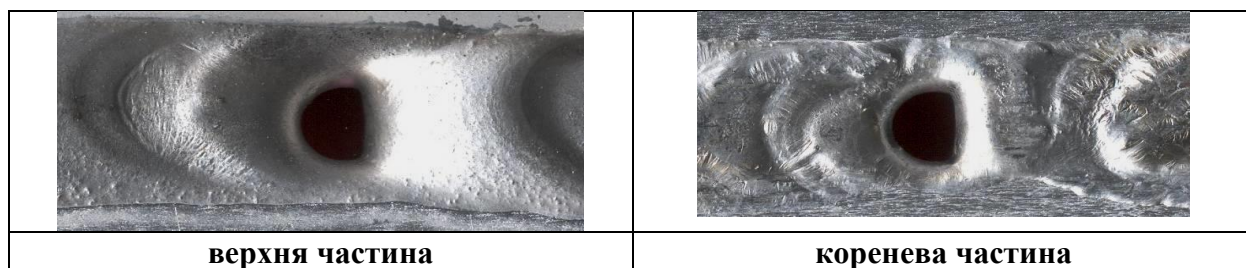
Верхня та коренева частина зварного з'єднання листів товщиною 6 мм сплаву АМгб, сформованого при плазмо-дуговому зварюванні у нижньому положенні з використанням сталеві підкладки з канавкою розмірами 10x1,0 мм.
